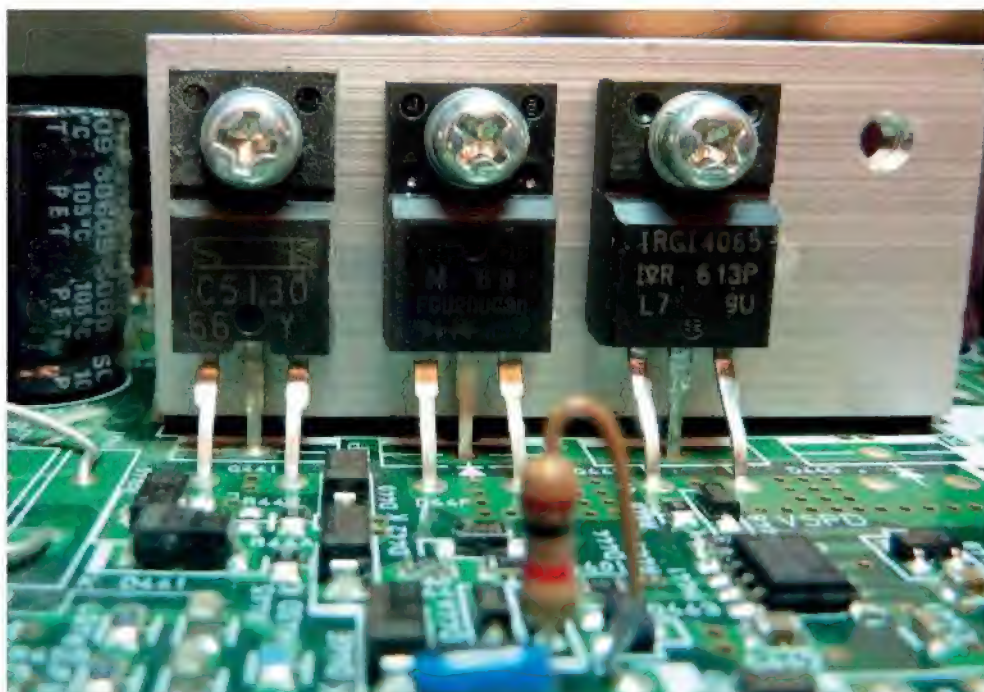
En arrière-plan, ponts de diodes montés sur dissipateur en aluminium
